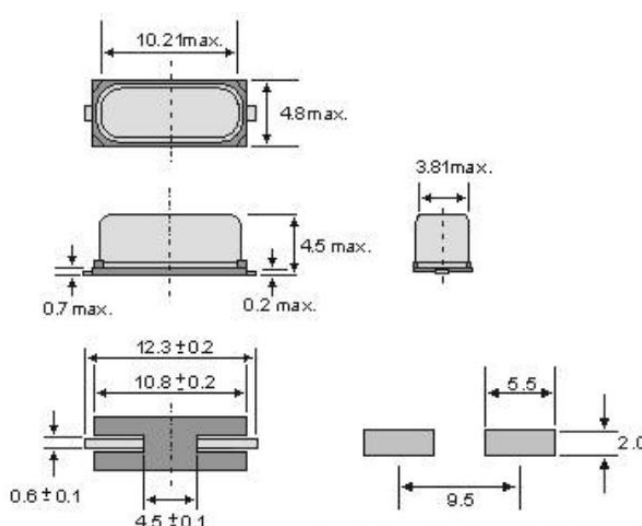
Габаритні розміри кварцевого резонатора HC-49SM
